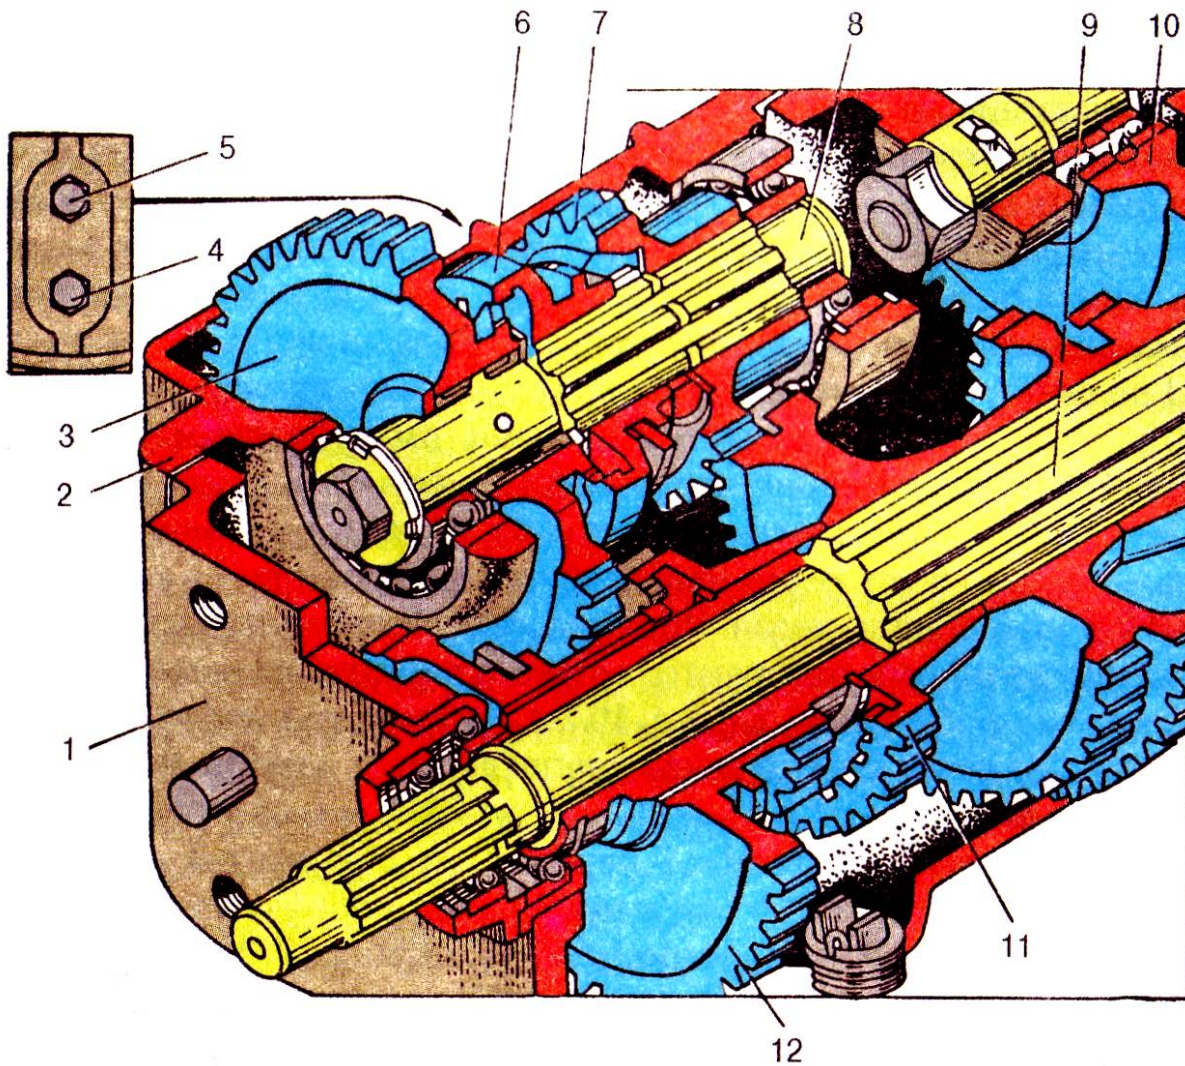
Редуктор коробки передач трактора ЮМЗ-6:
